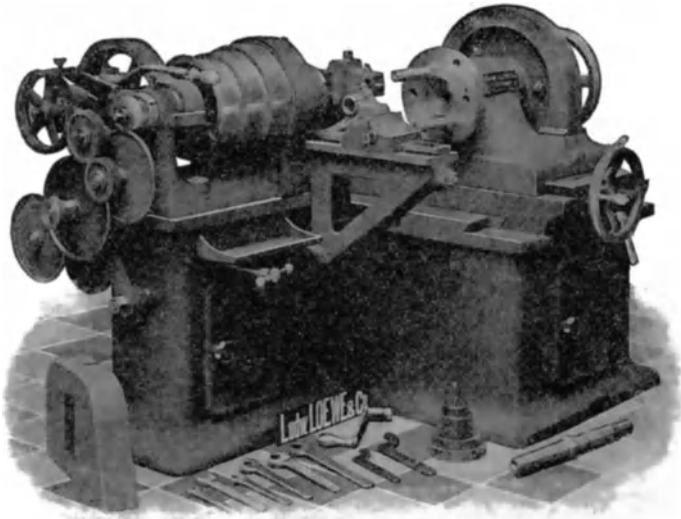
Die Rundfräsmaschine von L. Loewe & Co.
